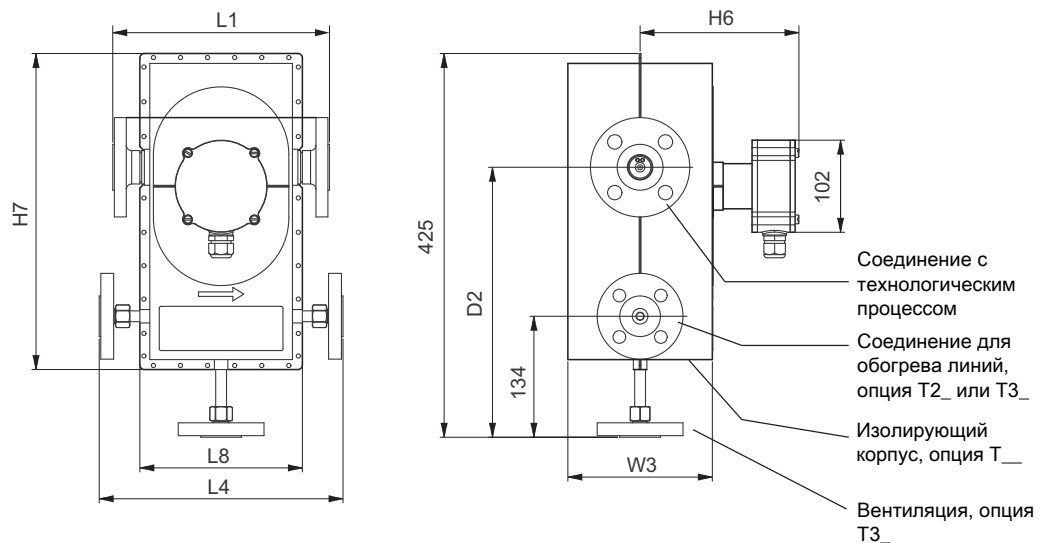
Размеры в мм: версия с изолирующим корпусом
